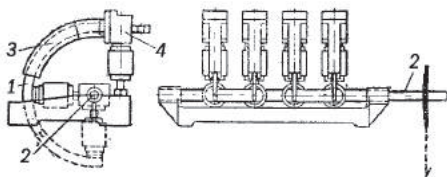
9 Трубчатый выключатель фирмы «Браун-Бовери» (1898 г.)
